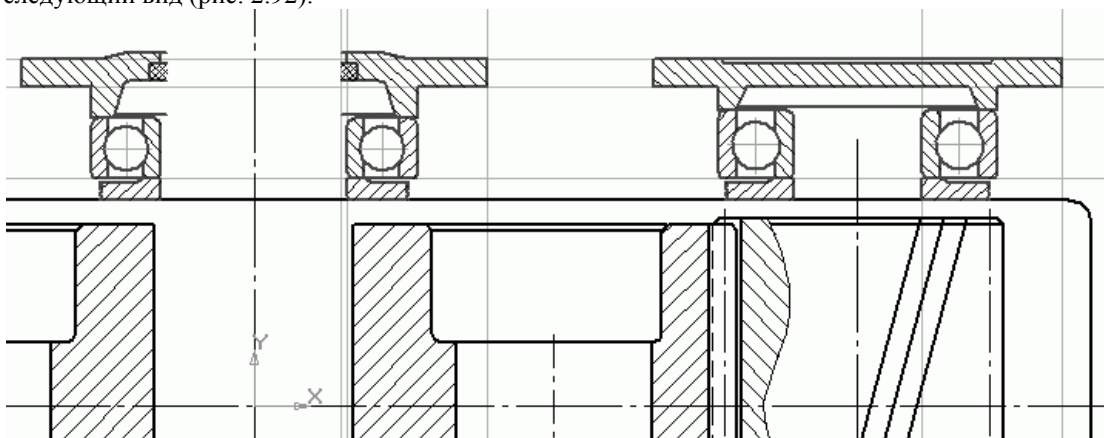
Подшипниковые узлы ведомого и ведущего валов
